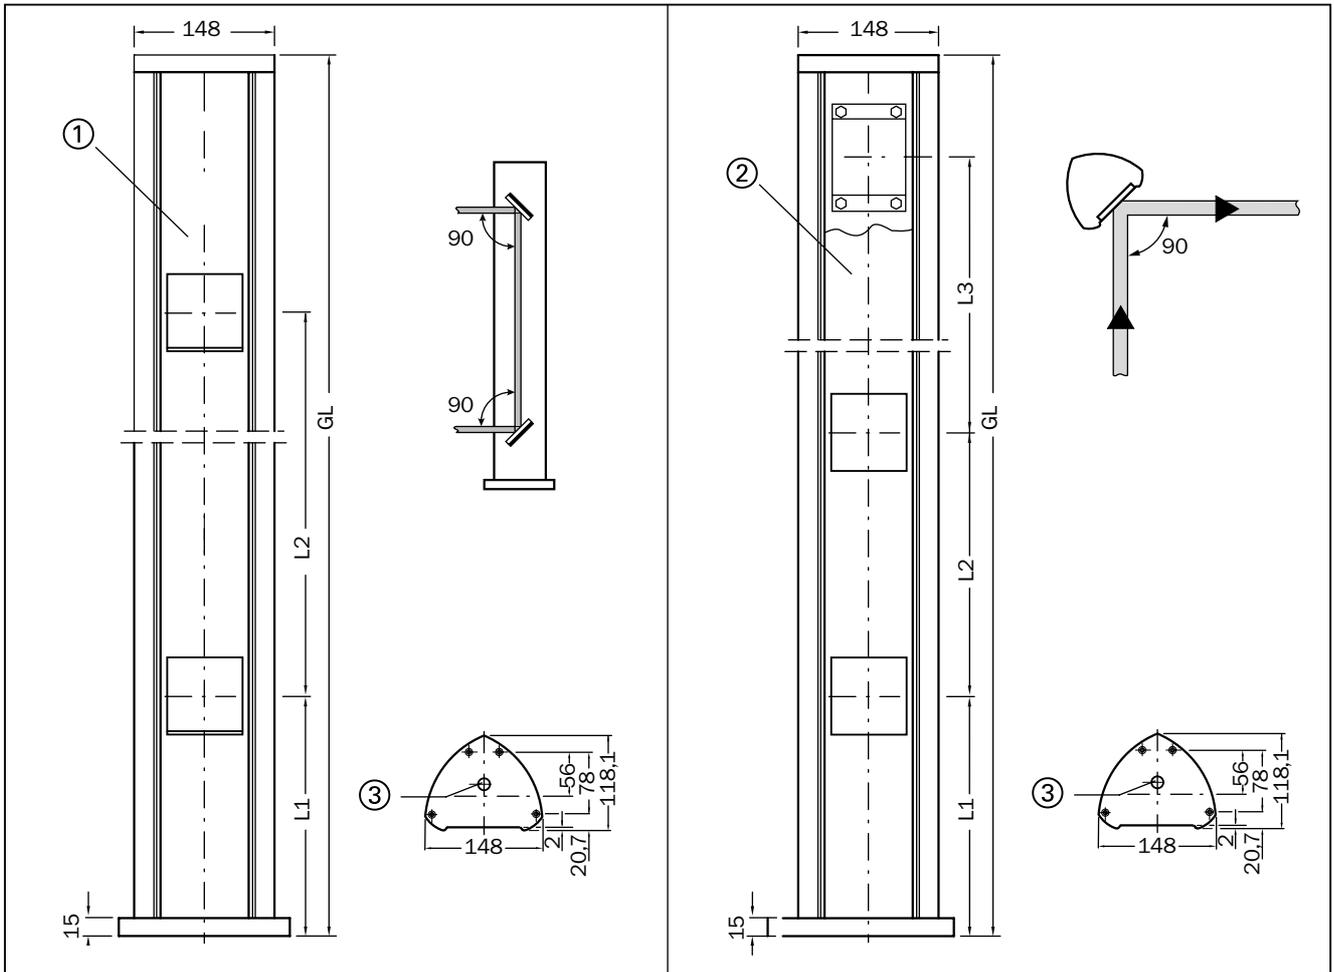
Plans et cotes d'encombrement des colonnes à miroirs de renvoi
